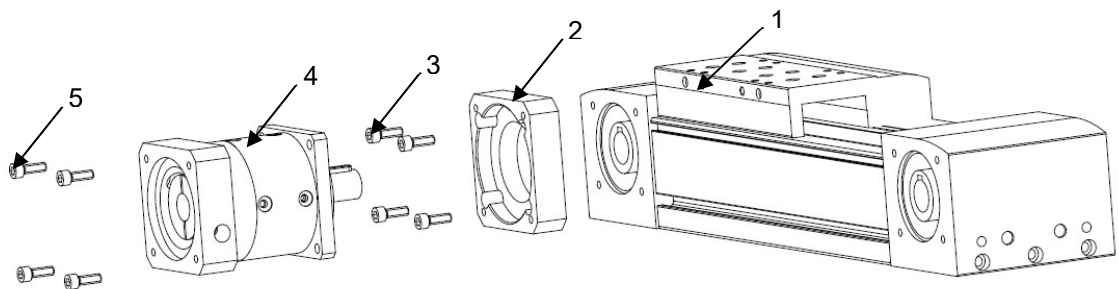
Установка редуктора с помощью монтажного комплекта модели FR-EGT
